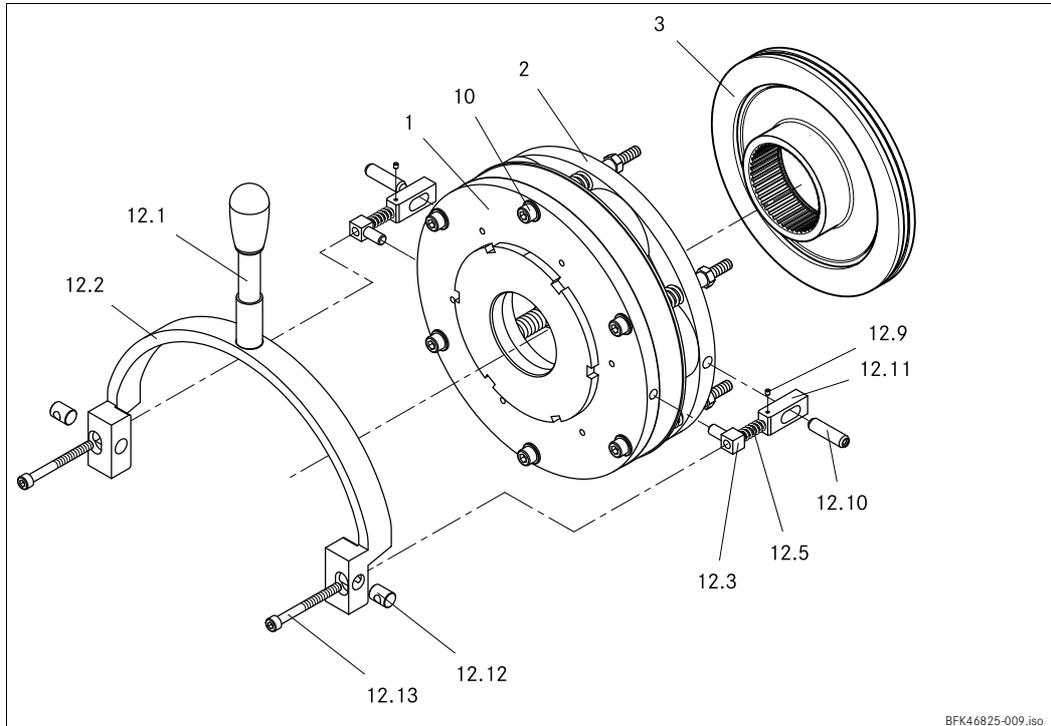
Handlüftungsmontage Bremsengröße 18-25
